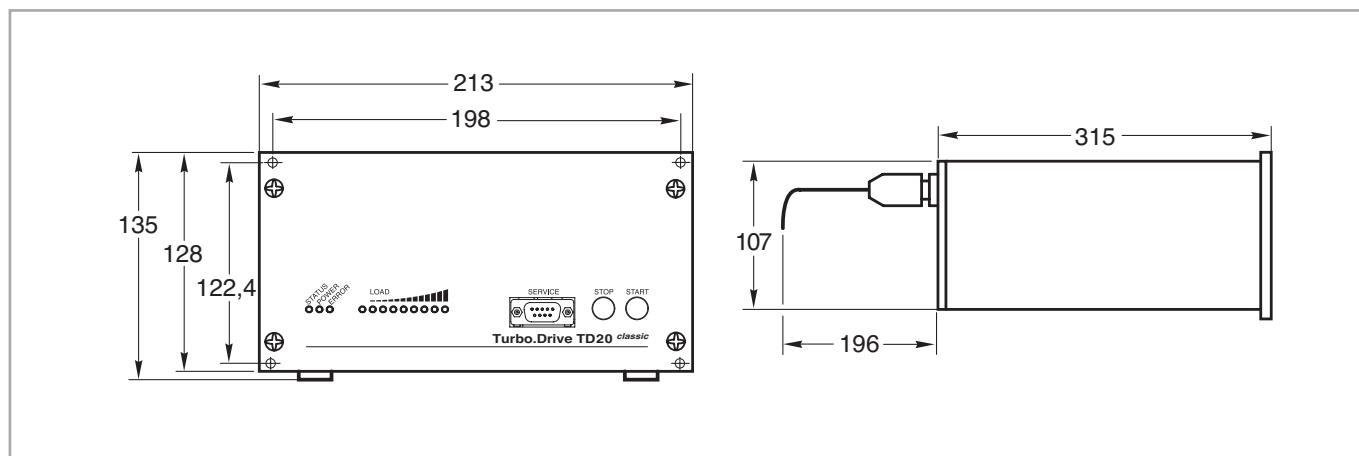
Maßzeichnung des Turbo.Drive TD20 classic, Maße in mm
